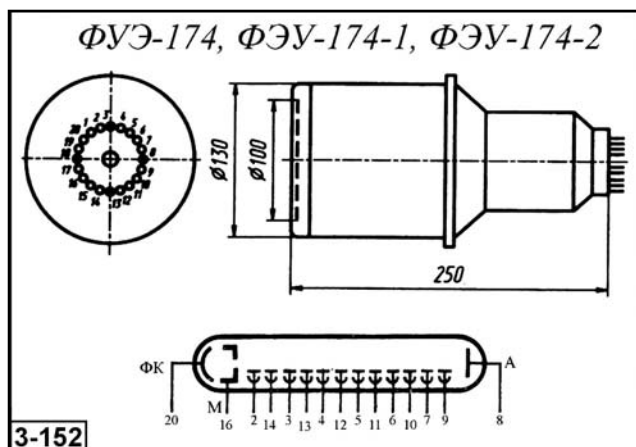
Внешний вид, габаритные размеры, схемы расположения штырьков, порядок их соединения с электродами и схема делителя напряжения фотоумножителей
